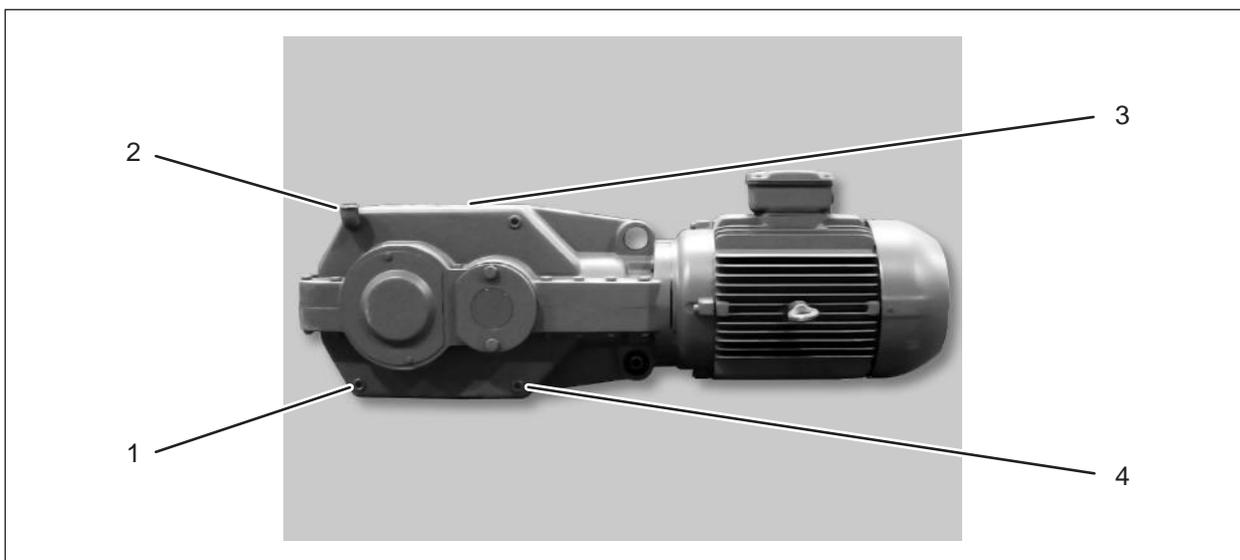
Accionamiento de la cinta con engranaje cónico de rueda frontal
